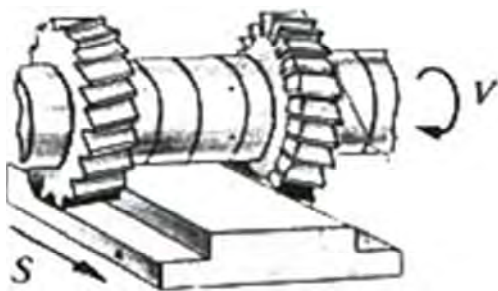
Фрезерование 2-х уступов набором дисковых двухсторонних фрез
